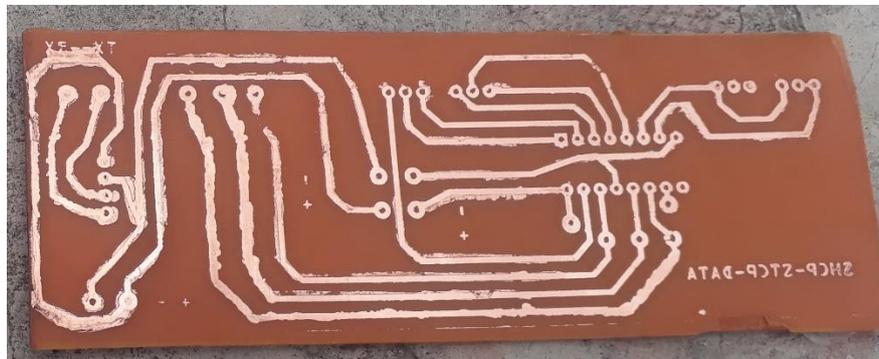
Tarjeta PCB para conexión de módulo HC-05 e IC 74595
